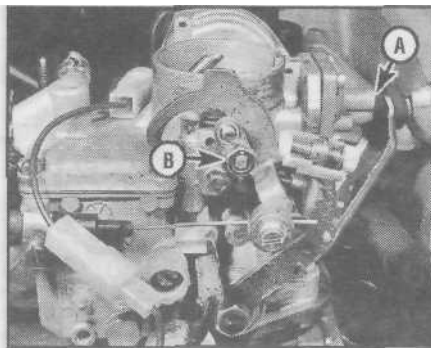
, б. Расположение винта регулировки зазора воздушной заслонки [А] и эксцентрика упора медленного прогрева
